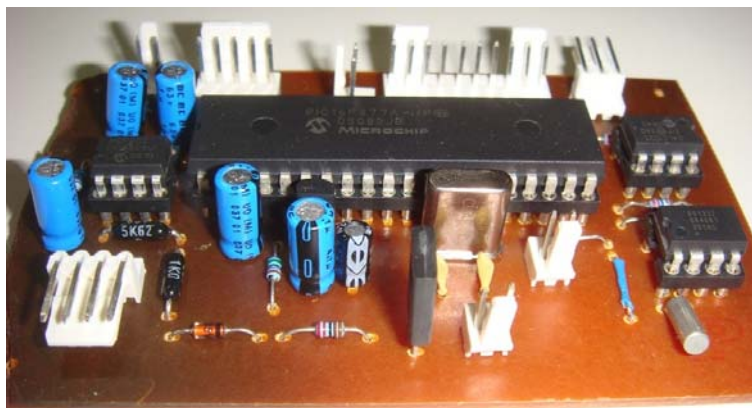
Placa de circuito impresso da EMA com os componentes eletrônicos soldados.
